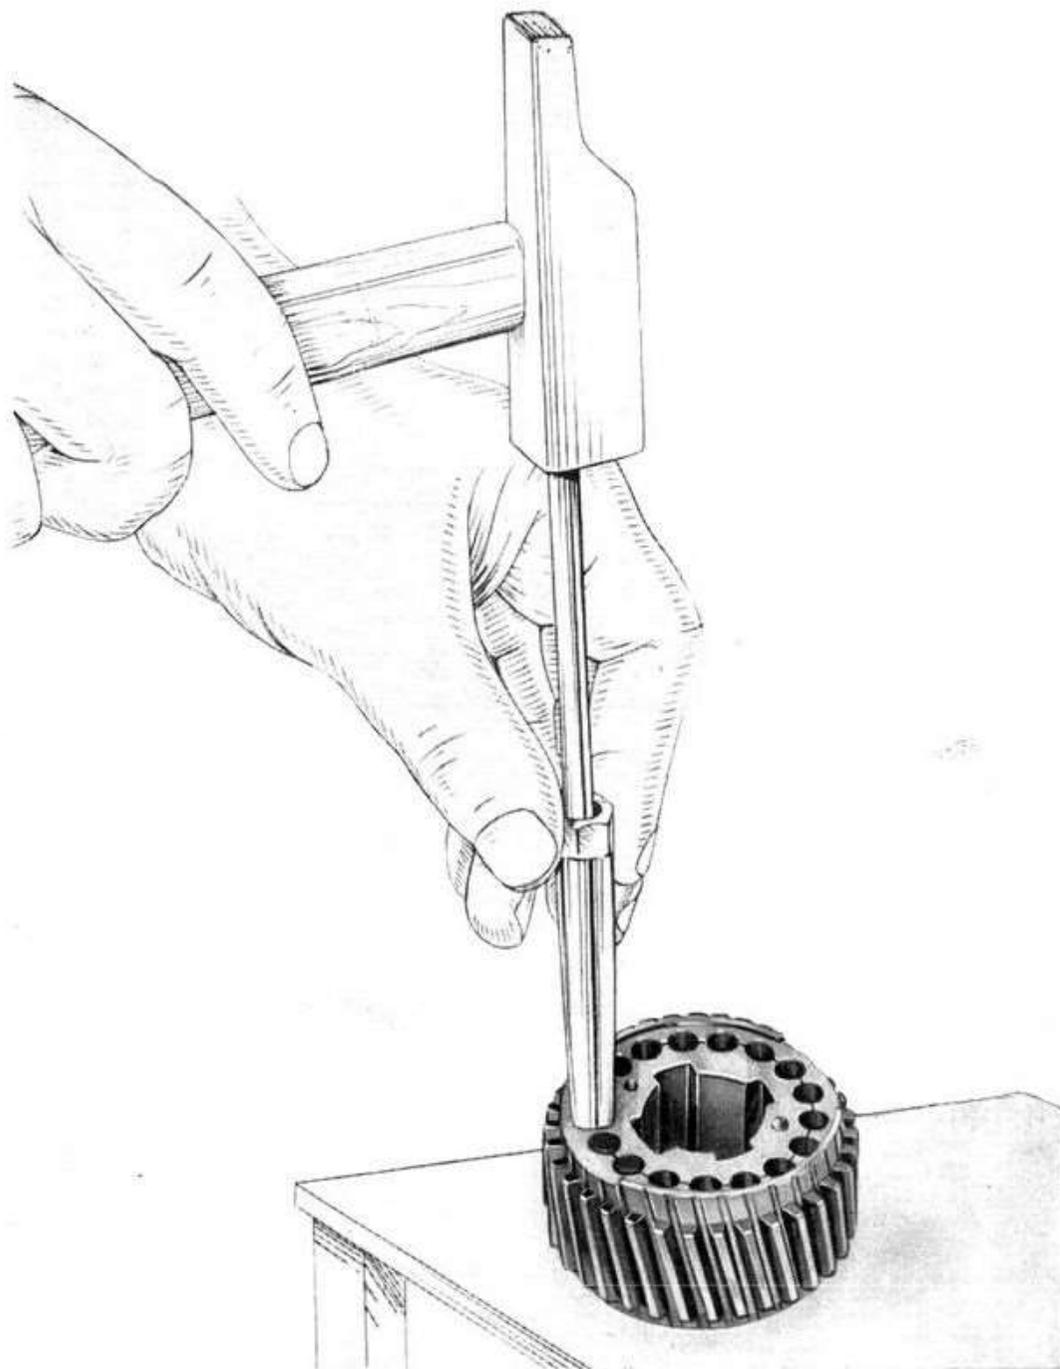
Montaggio dei cilindretti in gomma nel pignone elastico motore.
